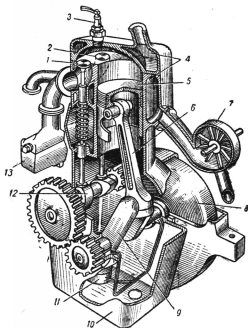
Четырехтактный одноцилиндровый карбюраторный двигатель:
